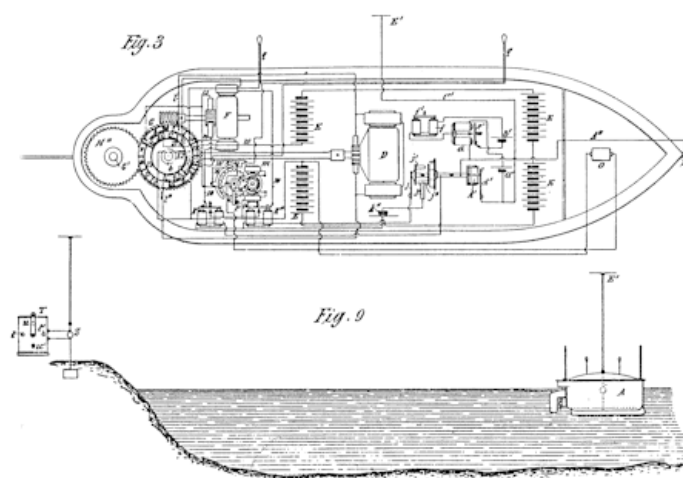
Planos del Teleautomaton (Fuente: vadebarcos.net)
